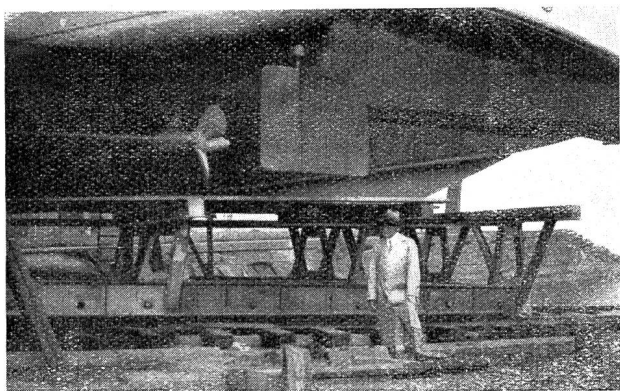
Zürichsee-Fähre Meilen-Horgen. Steuerruder mit Schraube.
